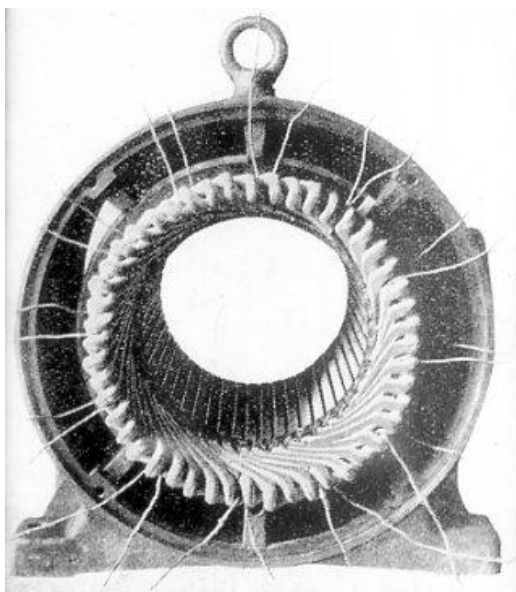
Станина и статор с обмоткой, уложенной в пазы: в верхней части корпуса расположен рым-болт, используемый для подъема двигателя при монтаже
